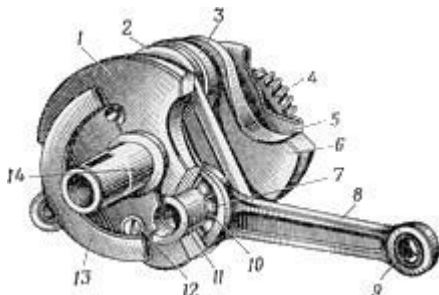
Коленчатый вал (кривошип) двигателя К-750:
